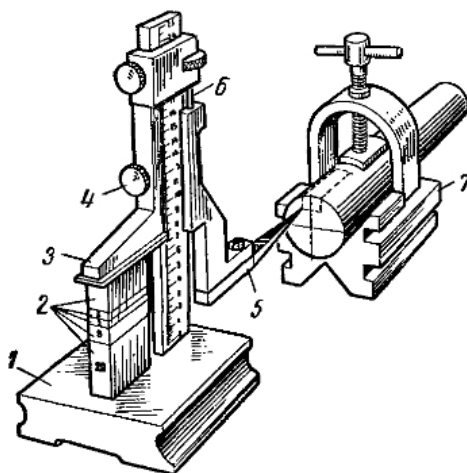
Разметка шпоночной канавки с применением плоскопараллельных концевых мер длины (плиток): 1 — измерительная поверхность. 2 — блок плиток, 3 — измерительная ножка, 4 — зажимный винт, 5 — чертилка. 6 — микрометрический винт, 7 — призма
